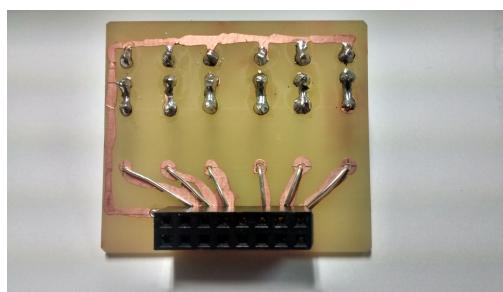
Vista del reverso de la placa, con los puntos de soldadura
